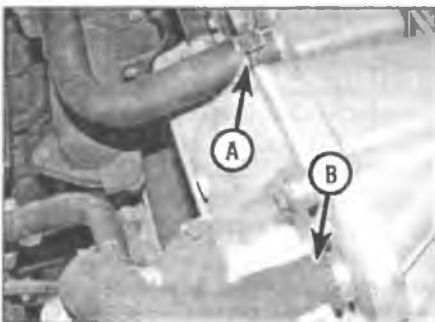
Отсоедините шланг вентиляции (А) и трубопровод EGR (В) от крышки головки цилиндров
